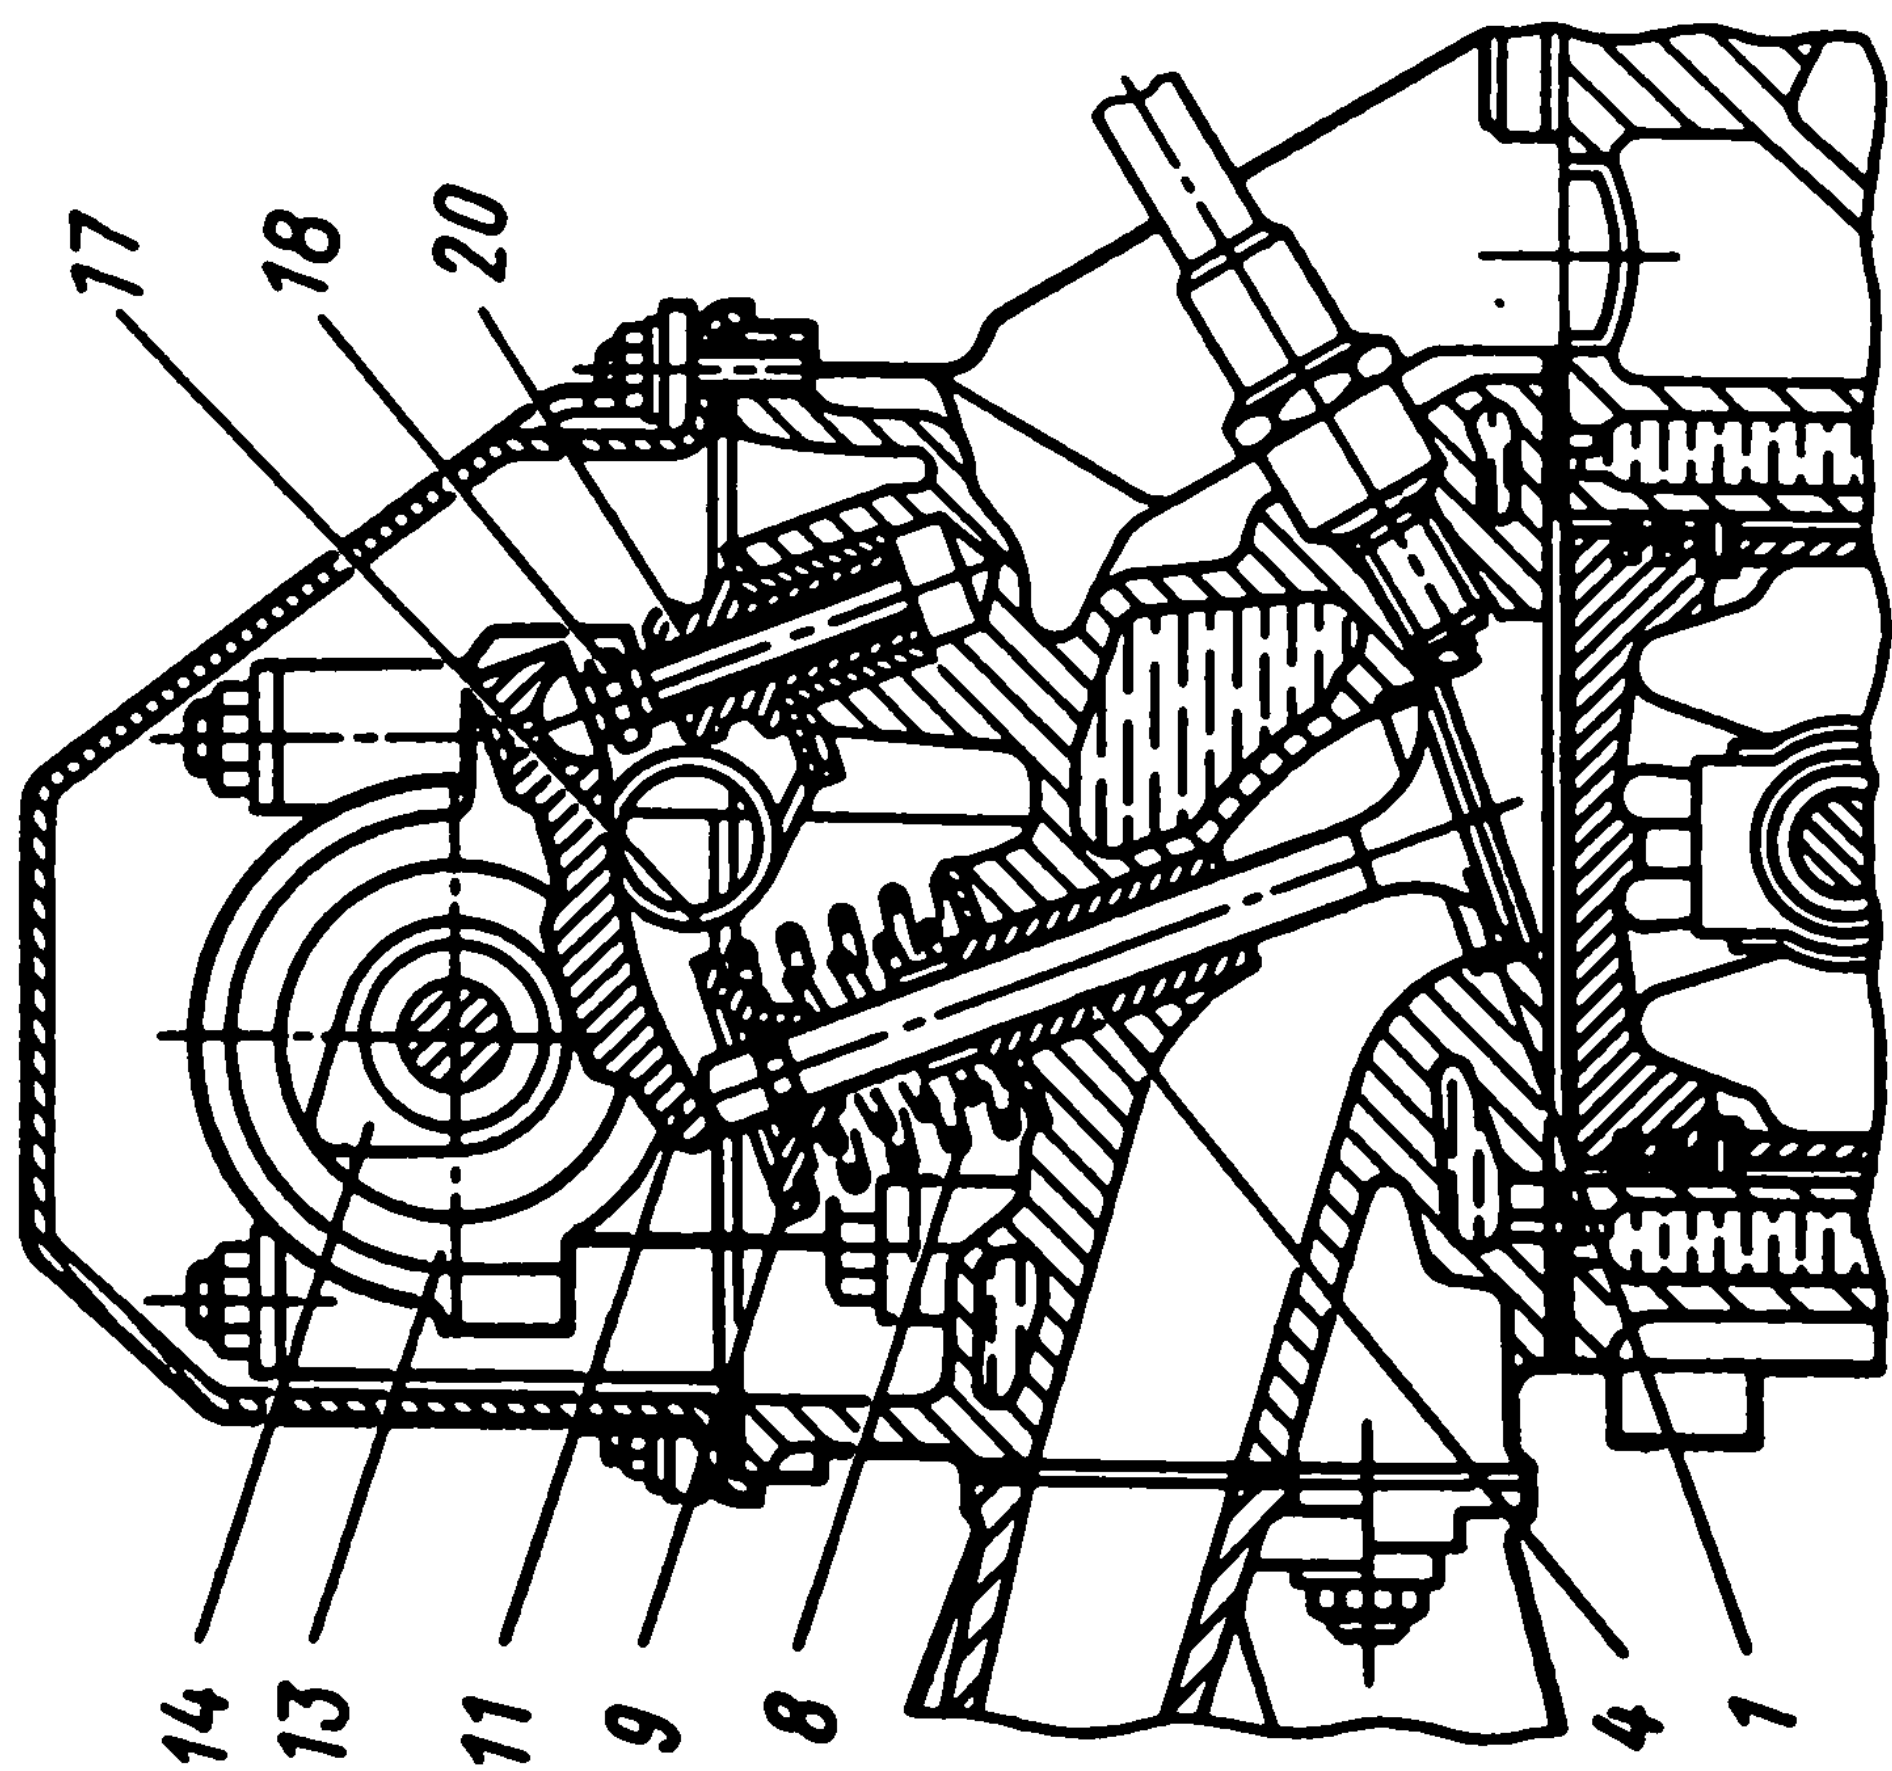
Газораспределительный механизм двигателя ВАЗ-2121
